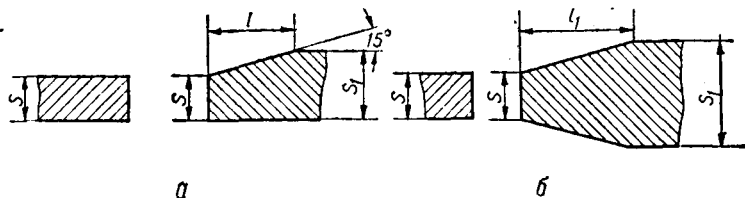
Схема подготовки кромок под сварку элементов разной толщины:
